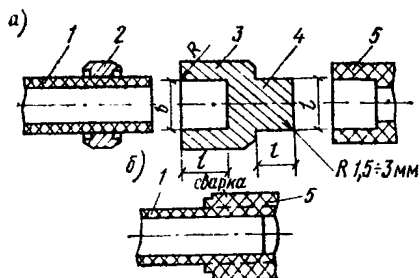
Приспособление для контактной раструбной сварки полиэтиленовых труб и фасонных частей
